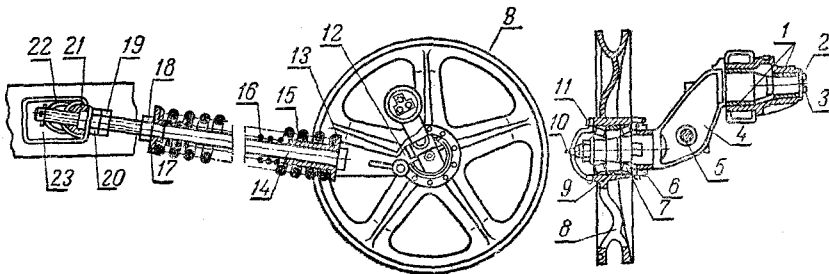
Направляющее колесо и натяжное устройство тракторов ДТ-75 и ДТ-75М:
